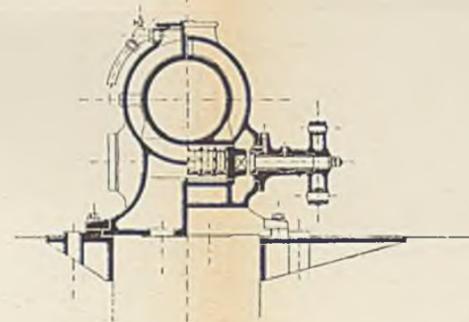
Schnitt durch den Hochdruck-Lufteylinder
